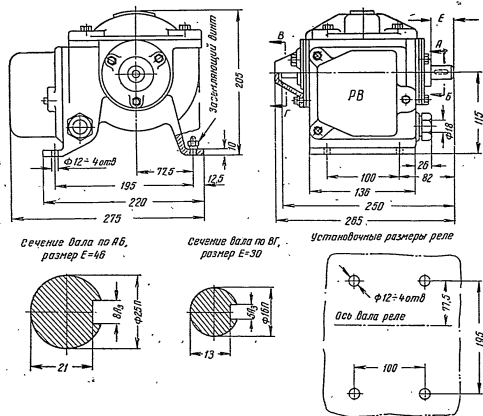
Габаритные и установочные размеры реле РМН 7011 и РМВ 7011 (знак РВ ставится только у реле РМВ 7011)
